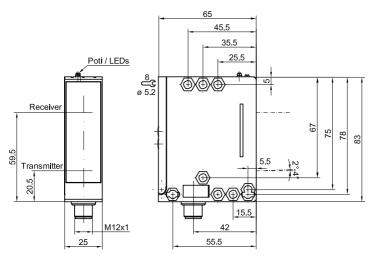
/ Illustr. 1 / Fig. 1 15300356
